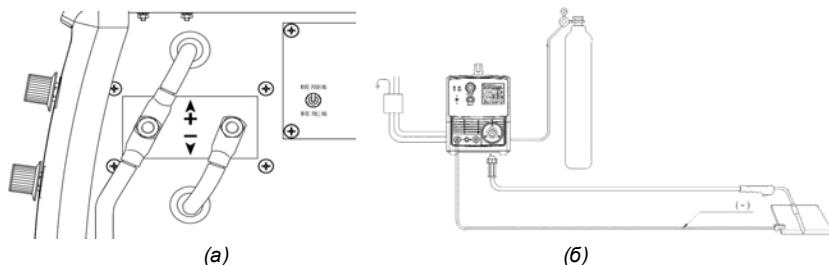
Полуавтоматическая сварка углеродистой стали углеродистой проволокой
